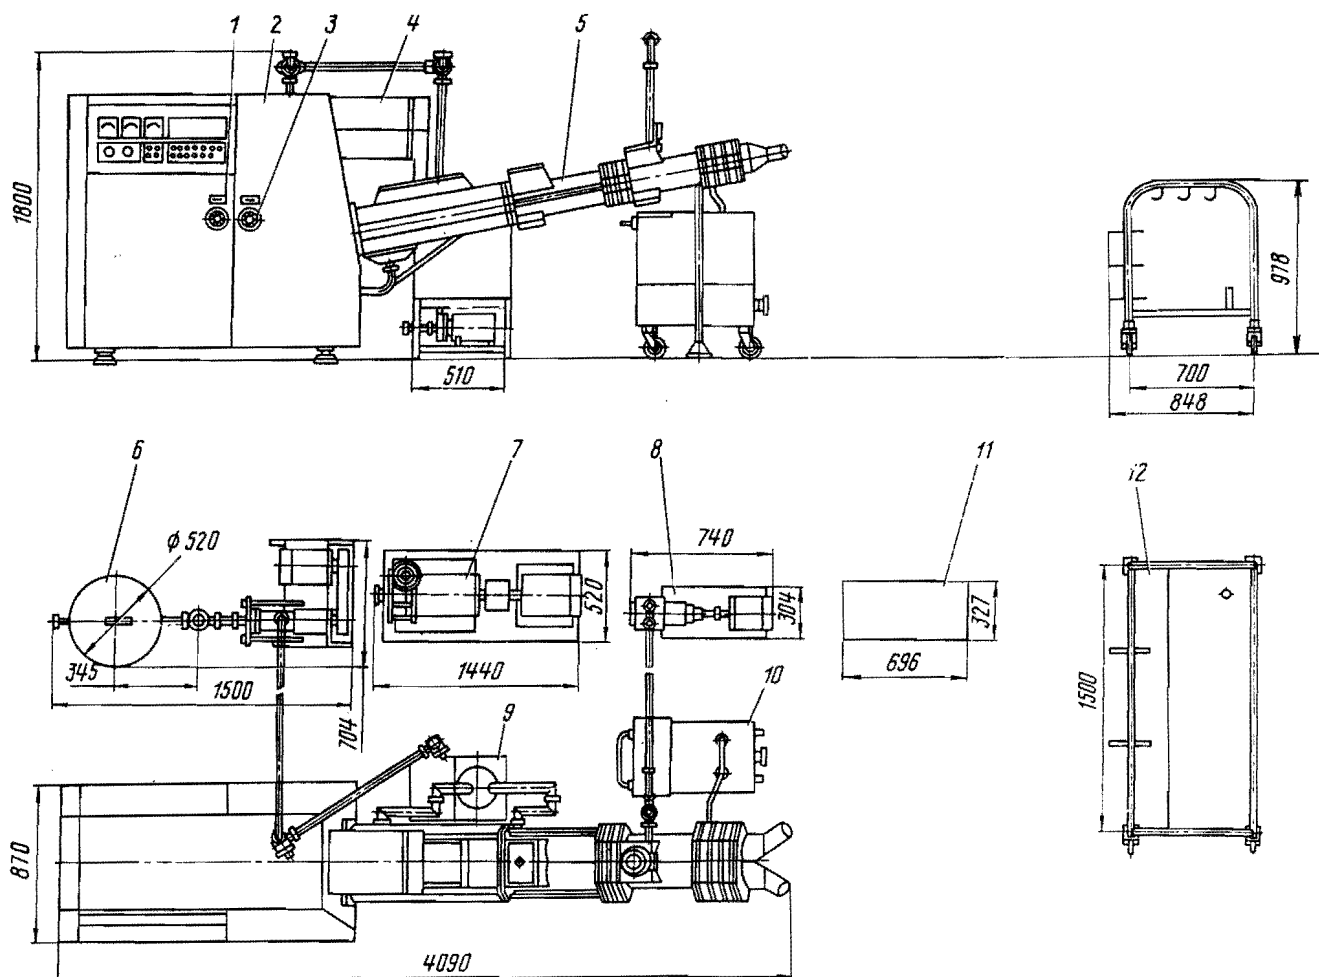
Общий вид маслоизготовителя марки А1-ОЛО/1:
